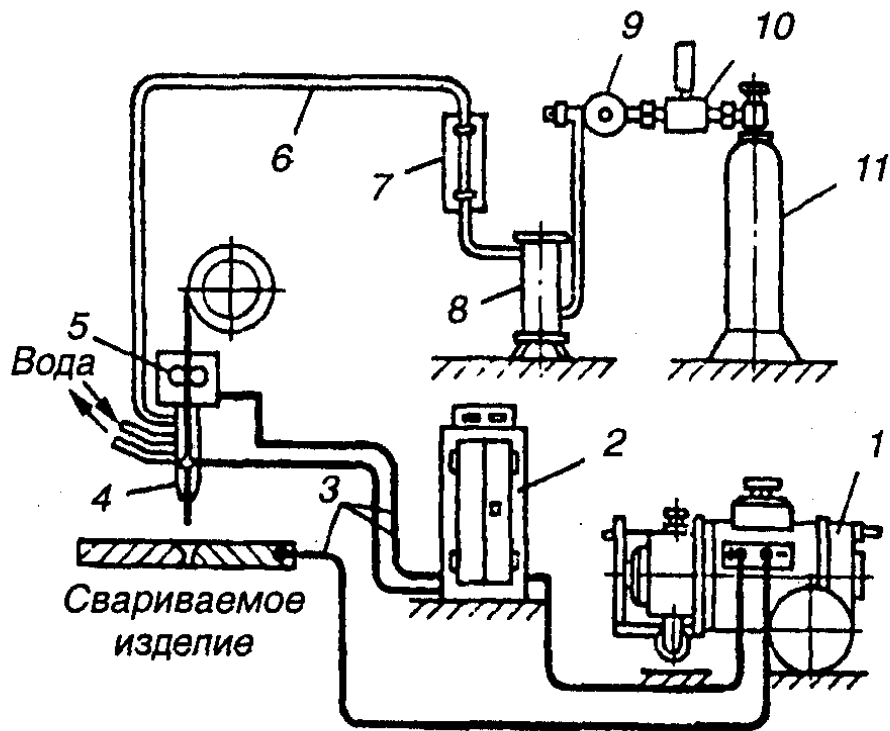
Пост полуавтоматической сварки электродом (в среде защитного газа):
